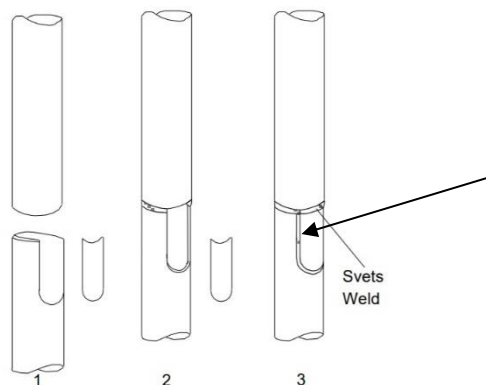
Lucksvetsen är en teknik att lägga svetsen från ett håll vid dålig åtkomlighet. En del av svetsen kommer då att gå i tubens längsled (se pilen).
